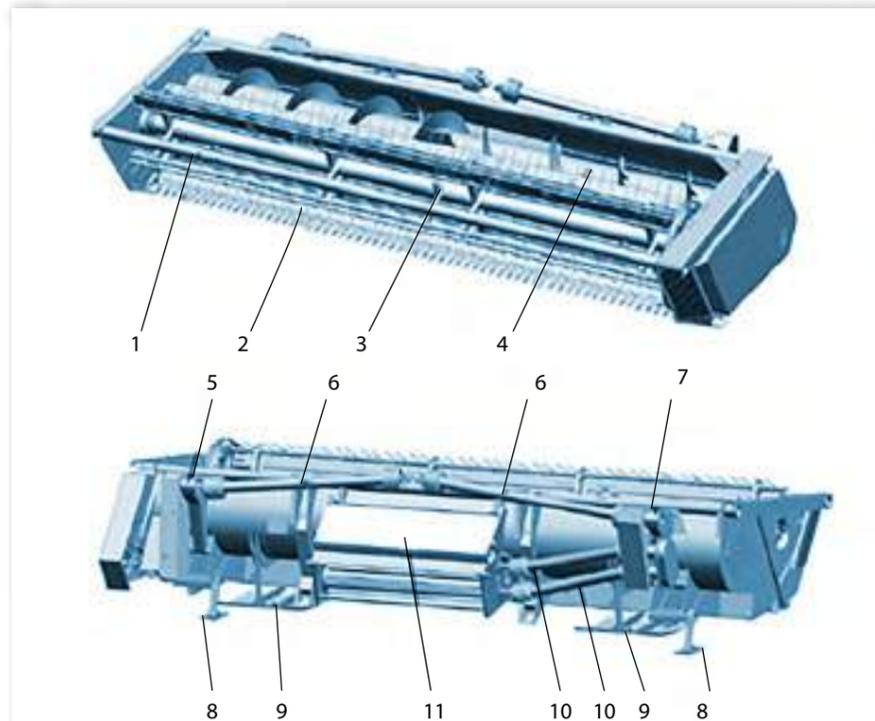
Косилка-плющилка КП-500: 1 — корпус; 2 — режущий аппарат; 3 — мотовило; 4 — шнек; 5 — левый контрпривод; 6, 10 — телескопический карданный вал; 7 — правый контрпривод; 8 — опора; 9 — башмак; 11 — плющильный аппарат
